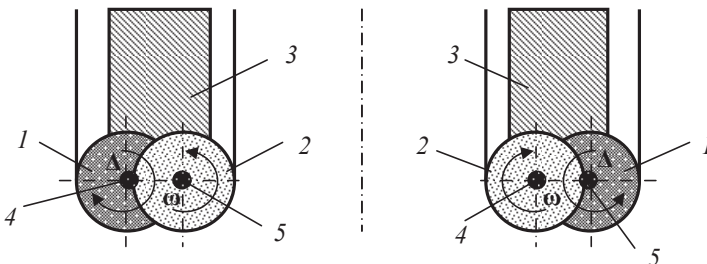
Коронка с вращающимися при бурении резцами: 1 – наружный резец; 2 – внутренний резец; 3 – корпус коронки с матрицей; 4 – ось вращения наружных резцов; 5 – ось вращения внутренних резцов
